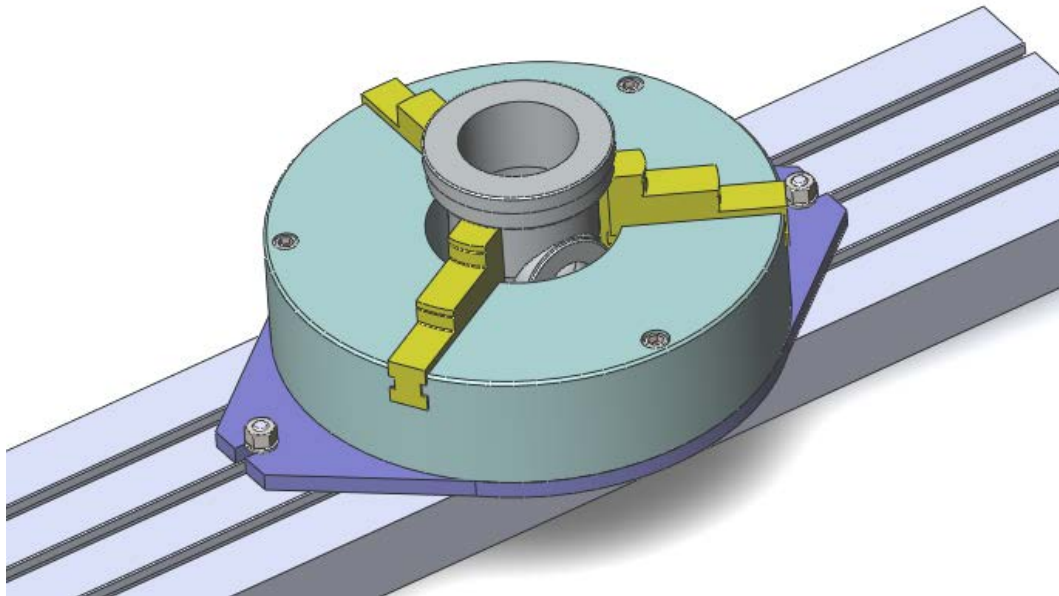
36 - Теоретична схема базування для обробки комплекту поверхонь 1
